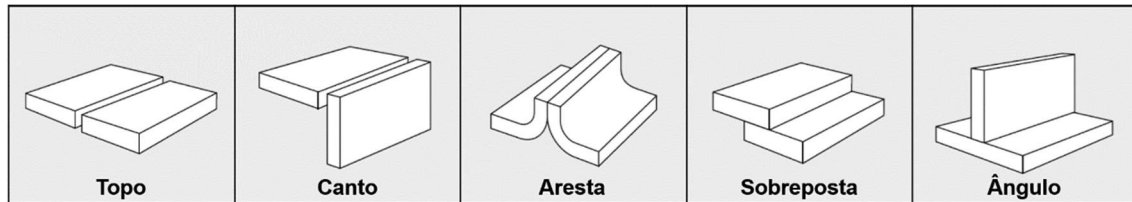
Tipos básicos de junta para soldagem. Adaptado (HIWT, 2012, p. 34).
